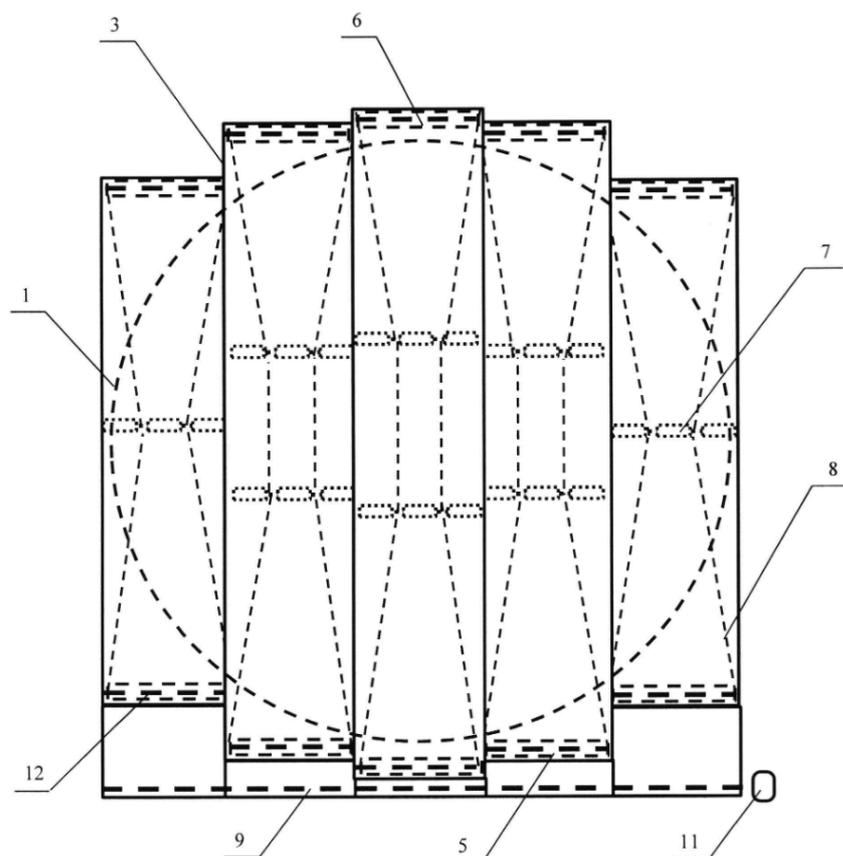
Вид устройства сверху: 1 – корпус резервуара; 2 – плавающая крыша; 3 – транспортерная лента; 4 – приводной барабан; 5 – натяжной барабан; 6 – оконечный барабан; 7 – ролики; 8 – несущий трос; 9 – верхний приводной вал; 10 – нижний приводной вал; 11 – движитель; 12 – ось; 13 – гибкий стальной армирующий элемент
